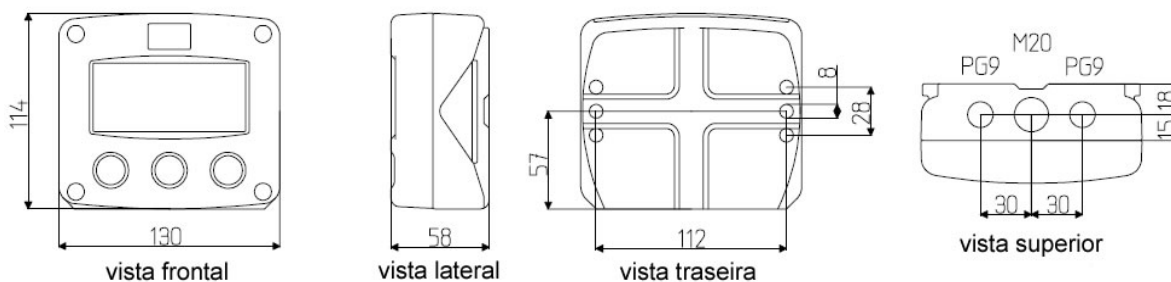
Dimensões para opção HÁ: Invólucro IP67 em alumínio com 2 conexões PG9 e 1 M20.
